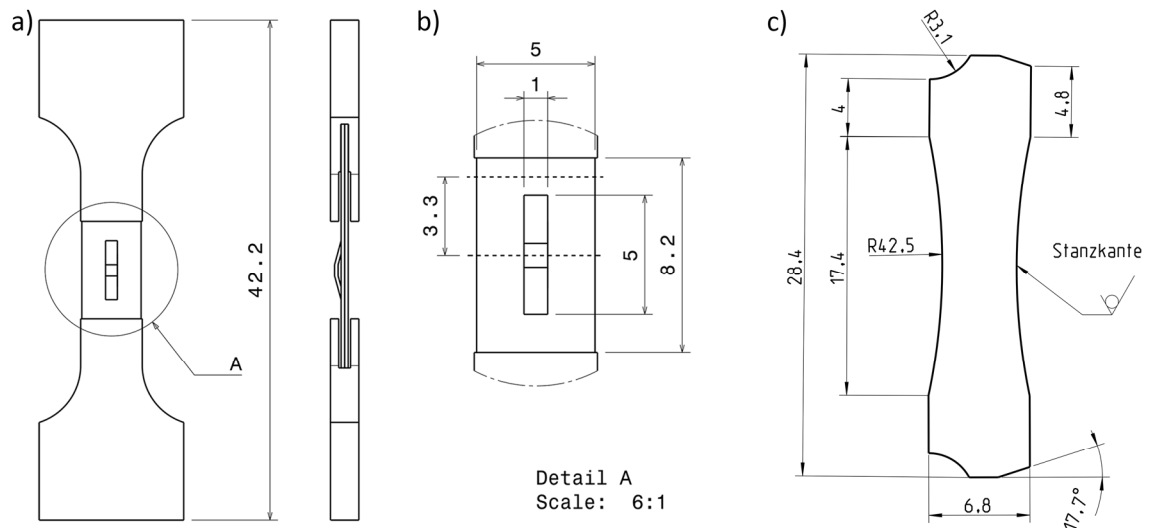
Bauteilproben, a) Clinchprobe mit Adaptern, b) Detail zum Clinchpunkt, c) Stanzprobe
